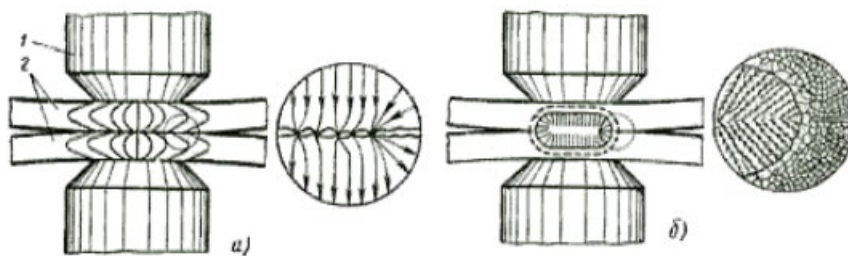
Схема процесу точкового зварювання. [29]
